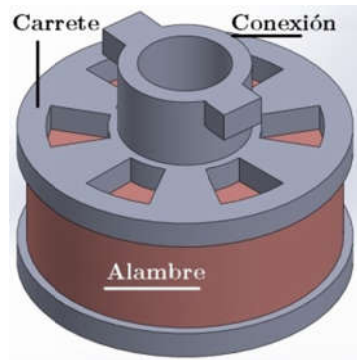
Ejemplo de carrete diseñado en SolidWorks, construido con impresora 3D, con una pestaña que permite montar y retirar la bobina del soporte.
